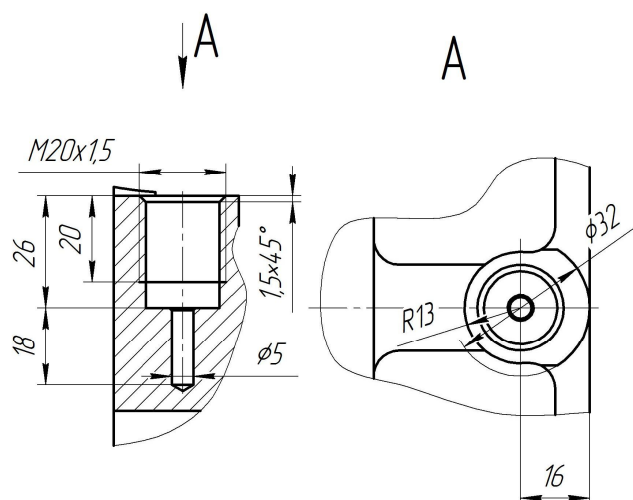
Присоединительные размеры под установку датчика контроля температуры подшипников для КМВГ 40-25-150Е.
